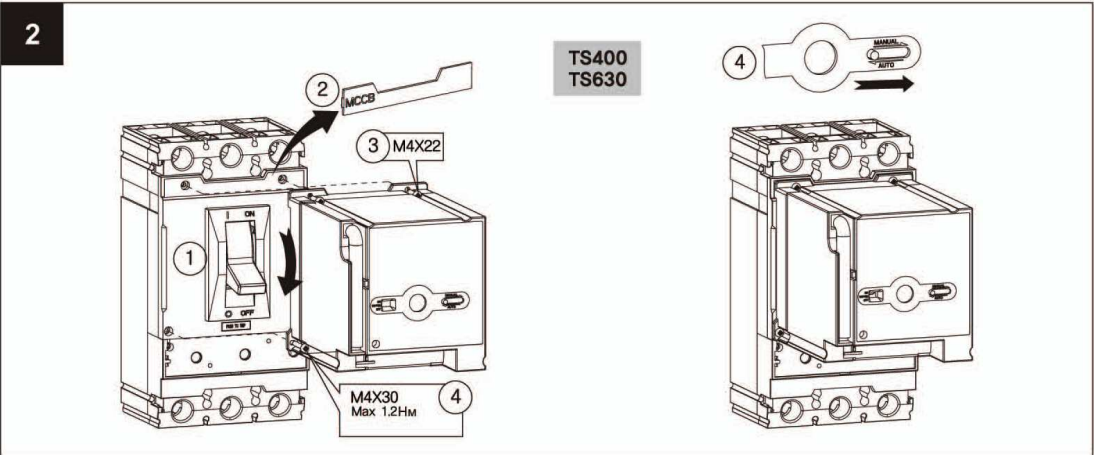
Установка моторного привода на выключатели TS400 и TS630
